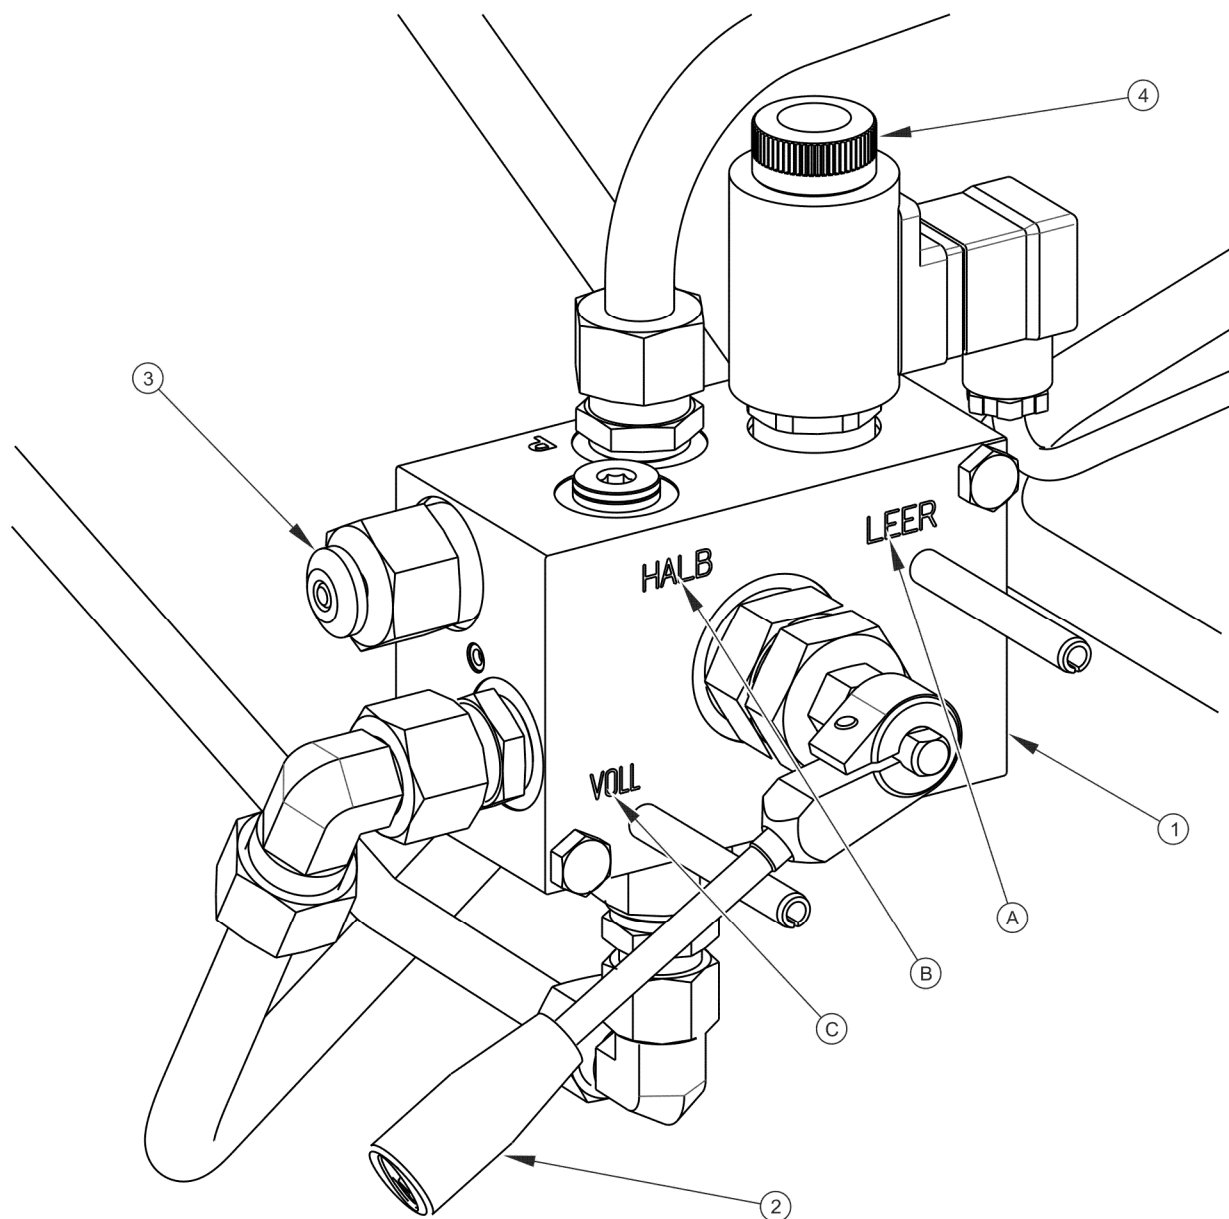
Konstrukce a schéma hydraulické brzdové instalace
